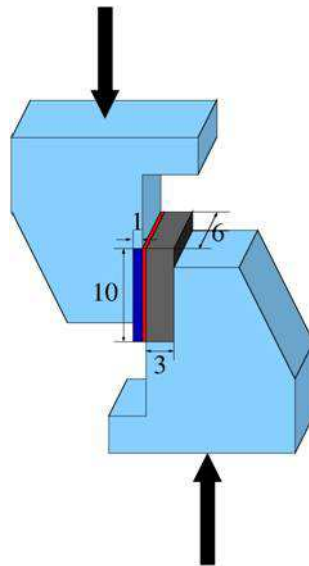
Representación esquemática de la configuración geométrica de las uniones cerámico-metal ensayadas en compresión ('single lap tests'). Las dimensiones de las muestras están en mm. El utillaje empleado y representado en color azul claro es metálico. Las flechas de color negro indican la dirección de aplicación de la carga.
